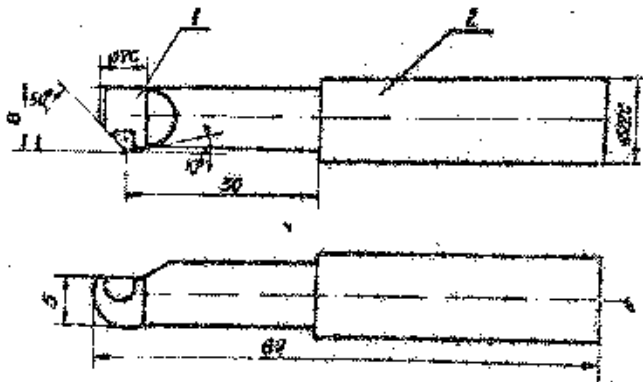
Сварной резец: 1 – вставка с режущим элементом из ПСТМ на основе нитрида бора типа ИС 005.00.01; 2 – державка
